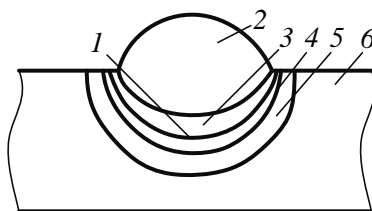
Схема зон сварного соединения:
